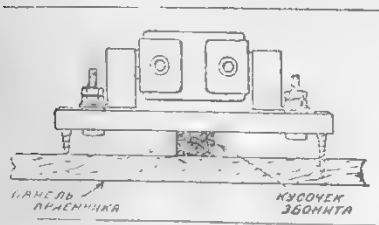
Монтаж держателя для конденсаторов и сопротивлений
